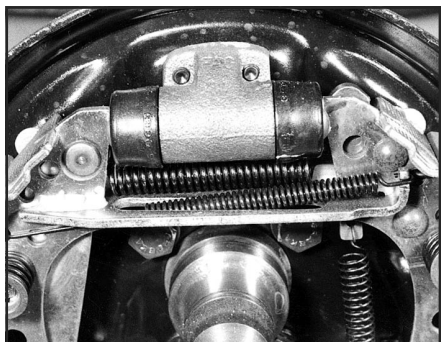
Колесный цилиндр, верхняя стяжная пружина и разжимное устройство
